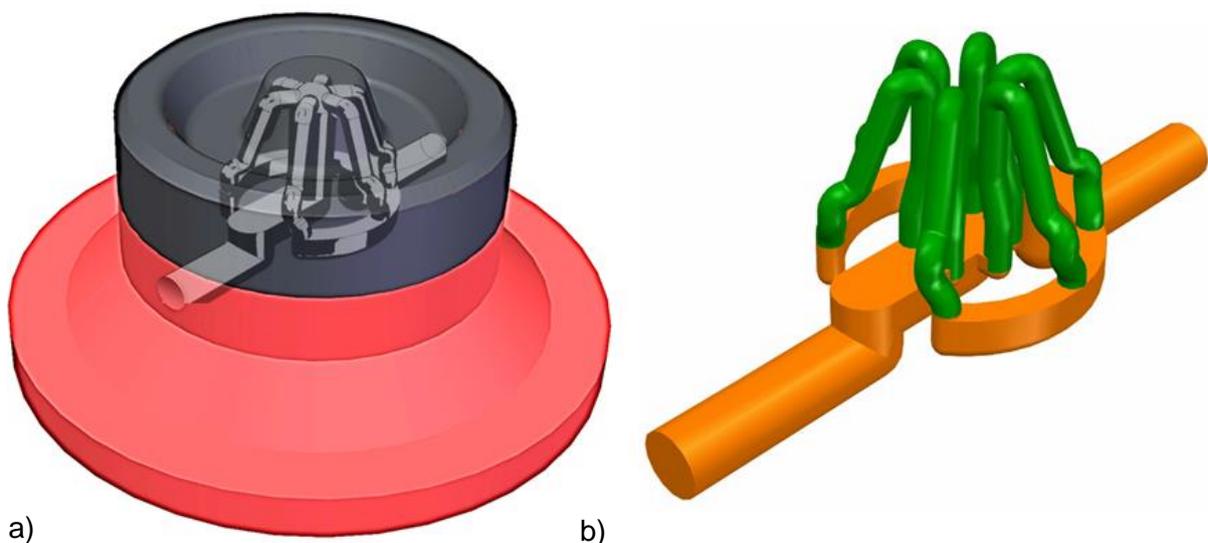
a) CAD-Modell des Schmiedewerkzeugs mit integrierten Kühlkanälen; b) Finale Struktur der Kühlkanäle
